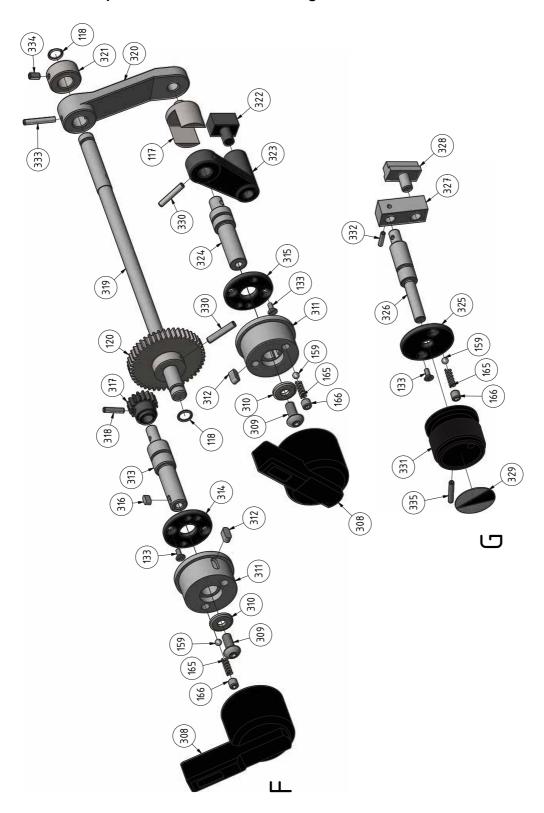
Getriebe Spindelstock 6-6 - Headstock gear 6-6
